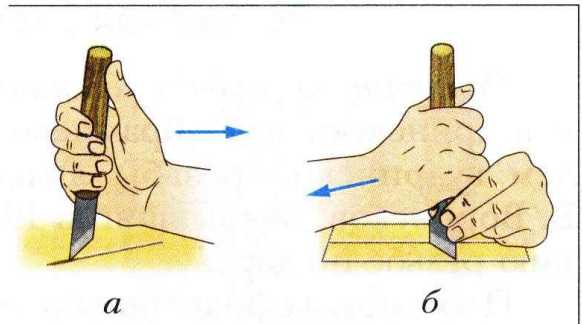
Положение инструмента при выполнении резьбы: а — одной рукой; б — двумя руками
